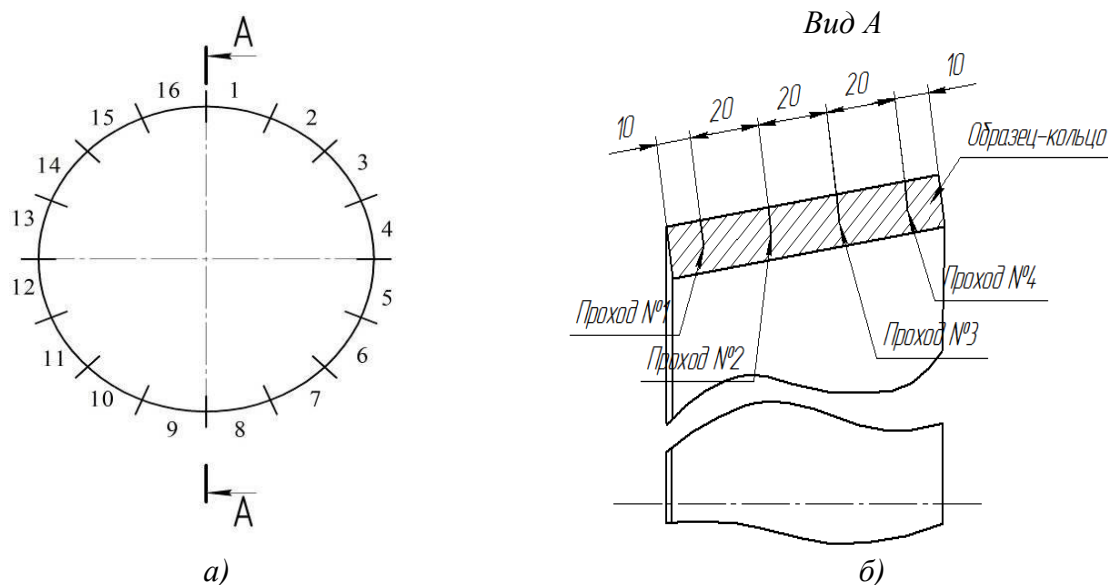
Схема реализации процесса сварки кольцевого шва:
